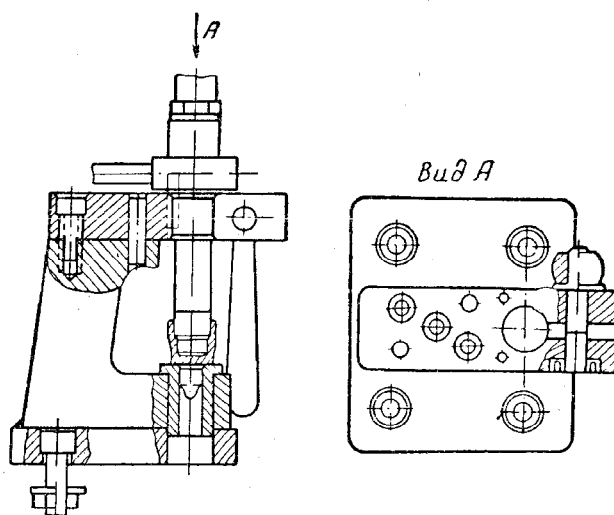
Приспособление ЛМ 9690-171 для центровки распылителя
